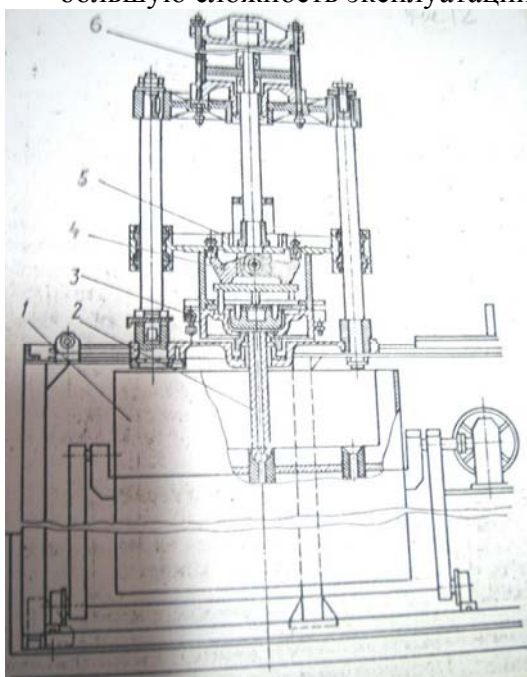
Установка модели ЛЭМД – 002 для получения отливок из алюминиевых сплавов.
